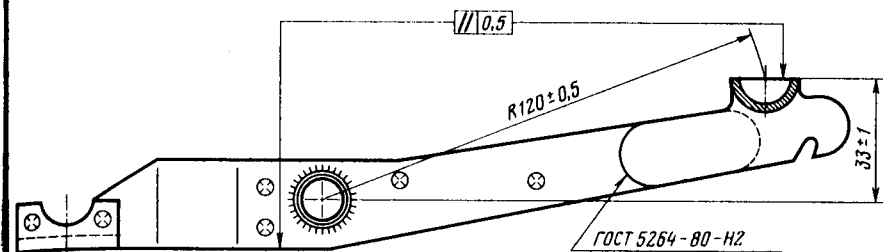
Приварка удлинителя к вилке выключения сцепления автомобиля 407
